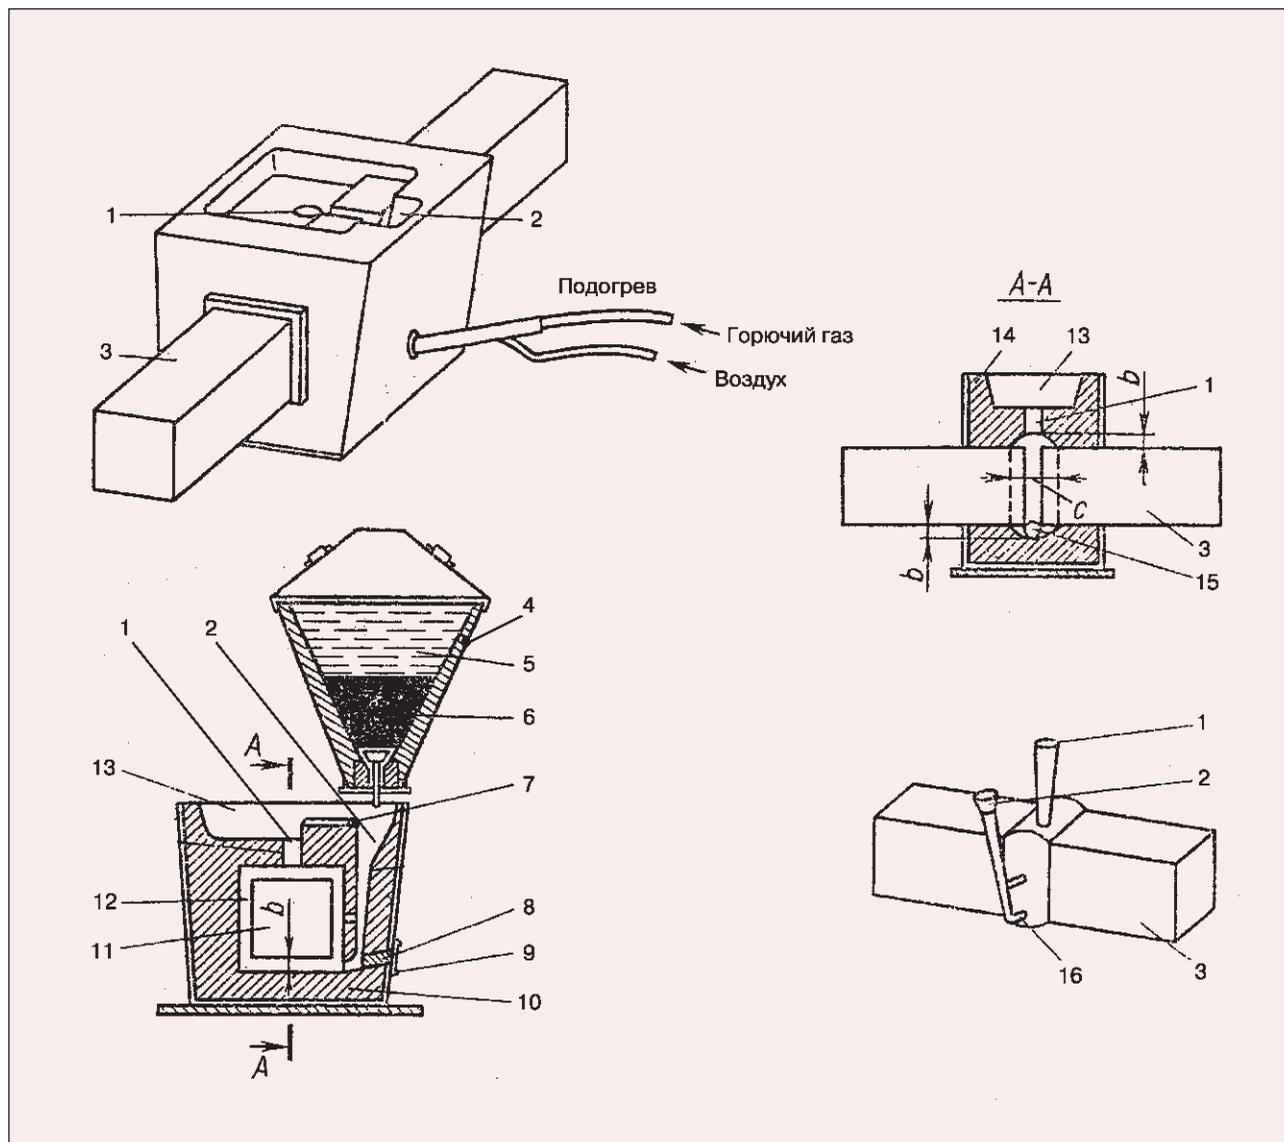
Схема термитной сварки: 1 — выпор; 2 — литник; 3 — свариваемая деталь; 4 — термитный тигель; 5 — термитный шлак; 6 — термитный металл; 7 — канал между выпором и литником; 8 — отверстие продувочного канала; 9 — железная или песчаная пробка; 10 — формовочный песок; 11 — сечение деталей; 12 — пространство для формирования усиления; 13 — шлаковая ванна; 14 — форма; 15 — продувочный канал; 16 — облив
